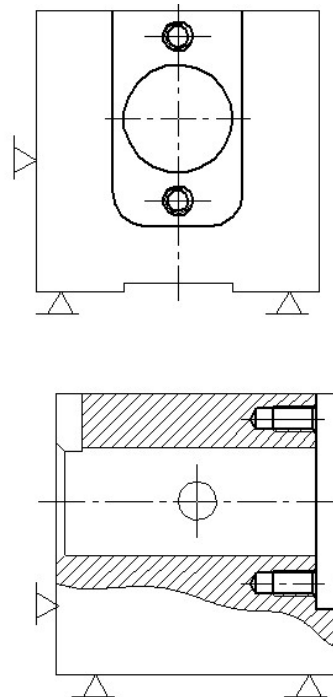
Схема базування деталі «Корпус АГЕ232»
